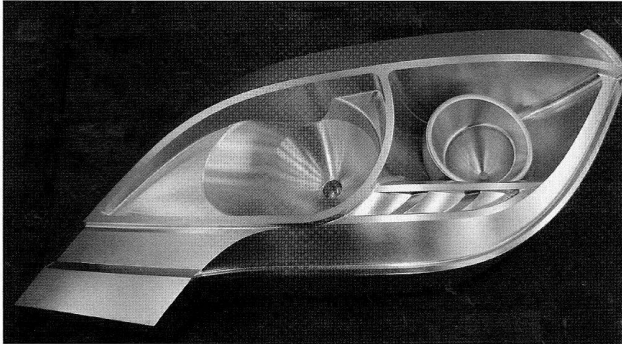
und 3b: Fünfschichtige Bearbeitung zur Erzeugung von komplexen Kavitäten. (Foto: GF AgieCharmilles)
